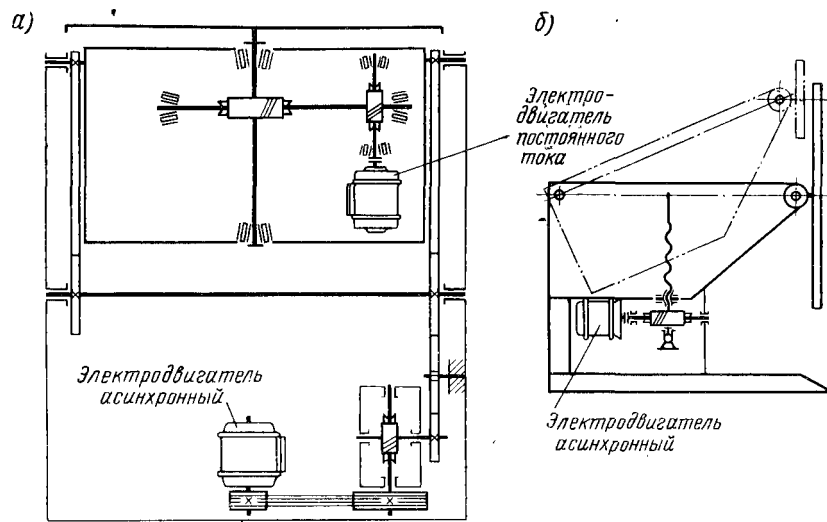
Кинематические схемы приводов универсального сварочного манипулятора:
